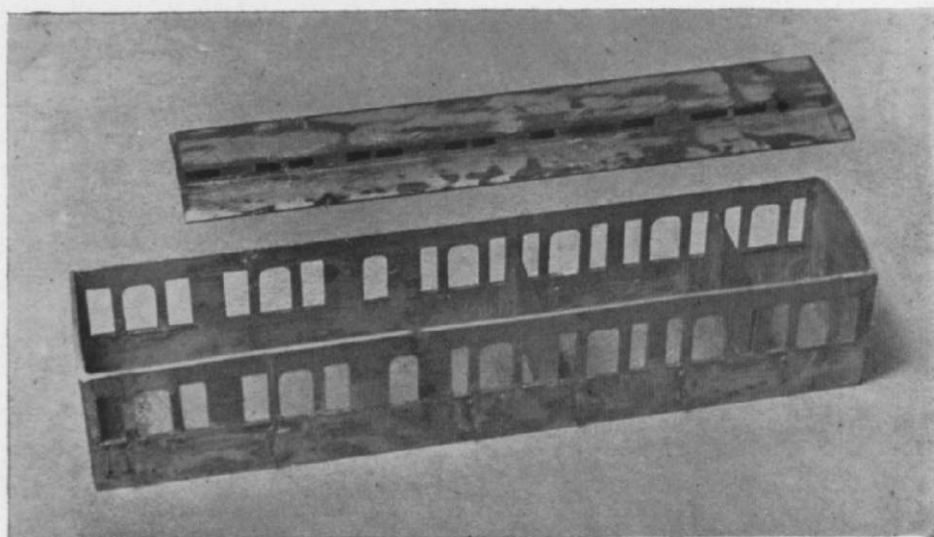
Wagenkasten aus 0,5 mm Zinkblech fertigen; vorteilhafter Messingblech, da besser lötbar.
